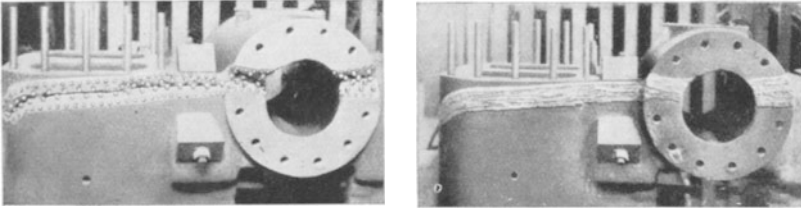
und 309. Kaltschweißung eines Gußzylinders.
